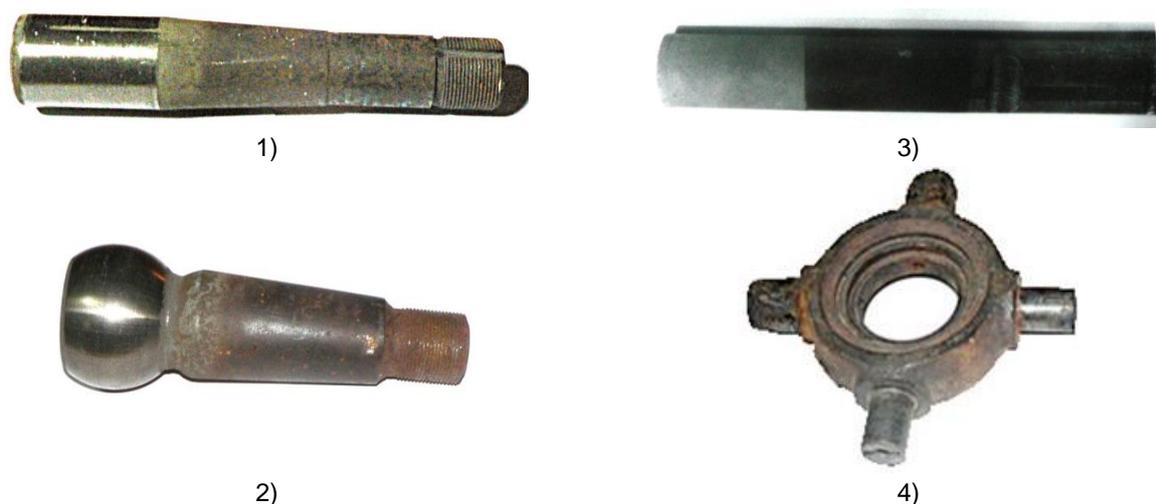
Детали-представители, восстановленные методами наплавки и нанесения покрытий: а – штырь поворотного кулака троллейбуса; б – палец шаровый реактивной штанги автомобиля «Камаз»; в – вал вилки муфты сцепления трактора ДТ-75; г – крестовина карданного вала трамвая Т-3М
